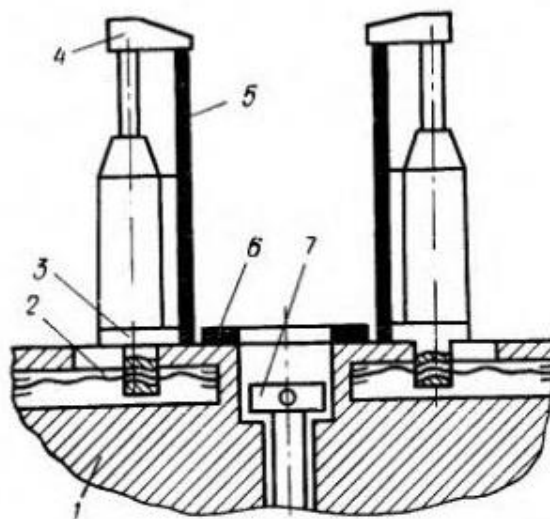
Схема кондуктора для сборки стержней коробчатого сечения
